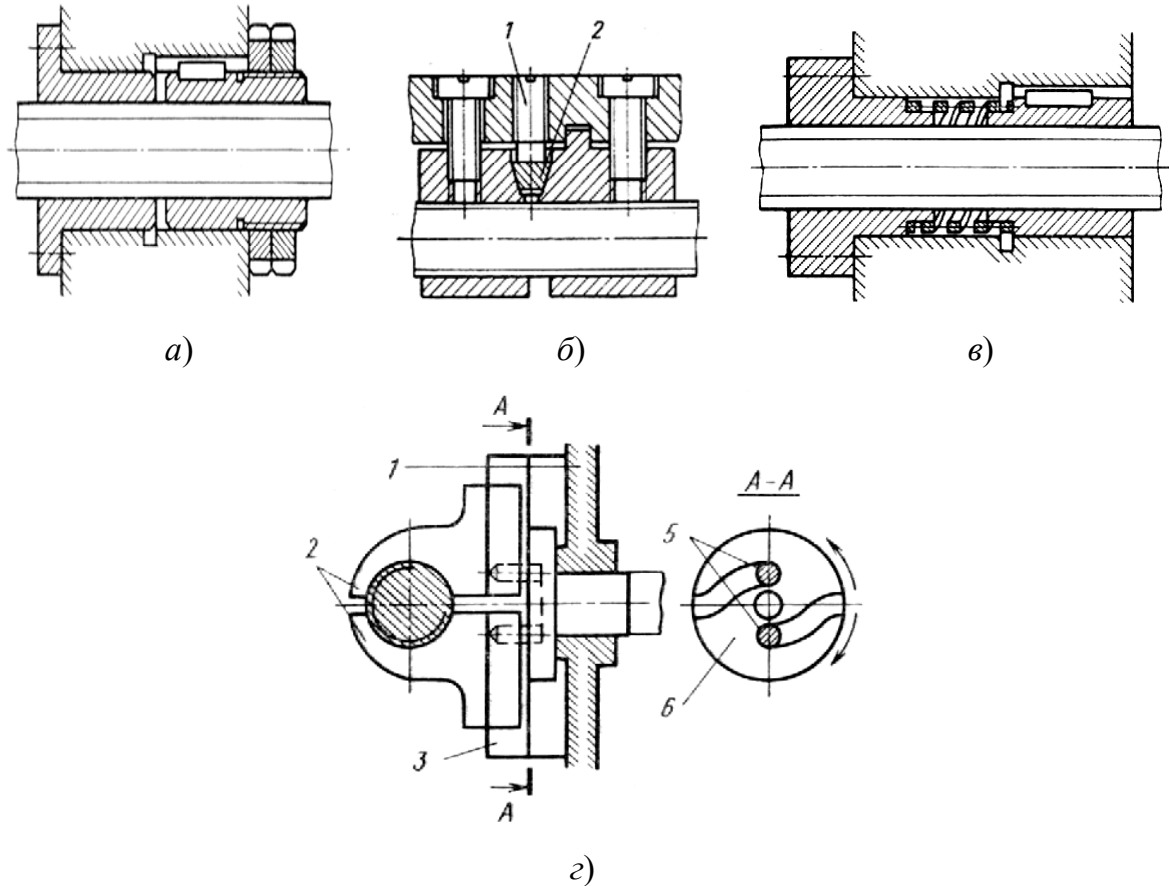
Эскизы конструкций регулирования зазора в резьбе:
